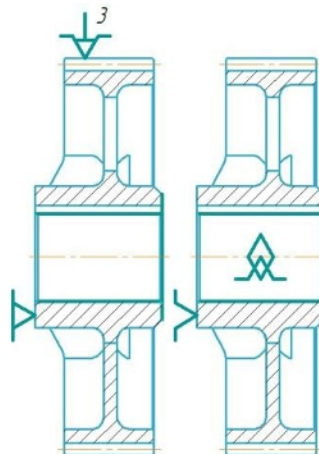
Умовна та теоретична схема базування зубчастого колеса
